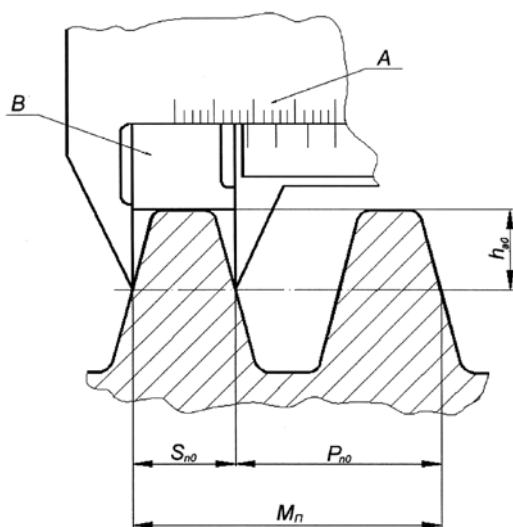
Схема измерения нормального шага винтовой спирали фрезы
